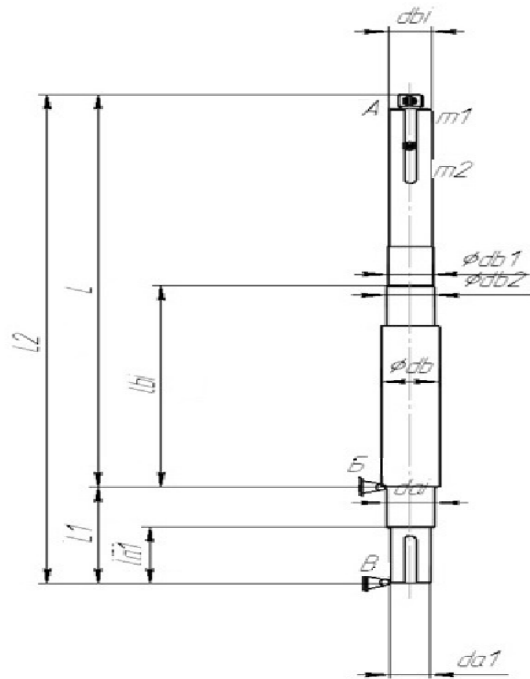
розрахункова схема консольного ступінчатого вала
